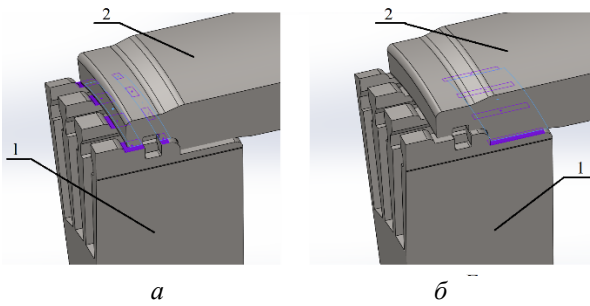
Поверхні з натягом: 1 – бочка ротора; 2 – бандажне кільце; а – посадка під носик; б – посадка на бочку ротора
